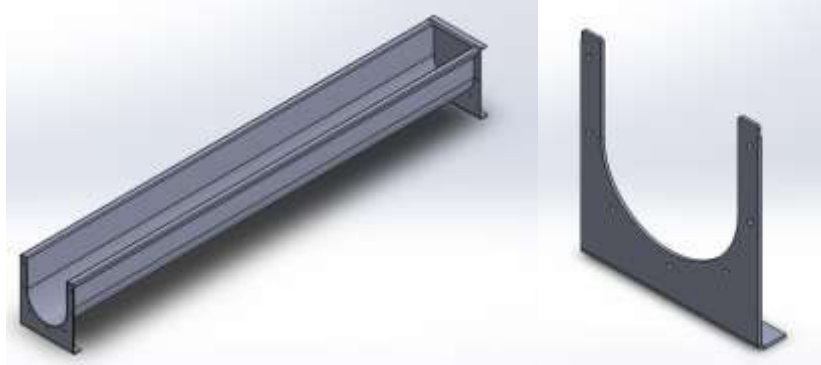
Estructura de plancha metálica (izquierda en conjunto, derecha aislada).
